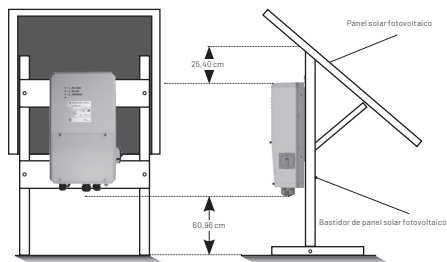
Montaje del dispositivo solar Pentek de Pentair
